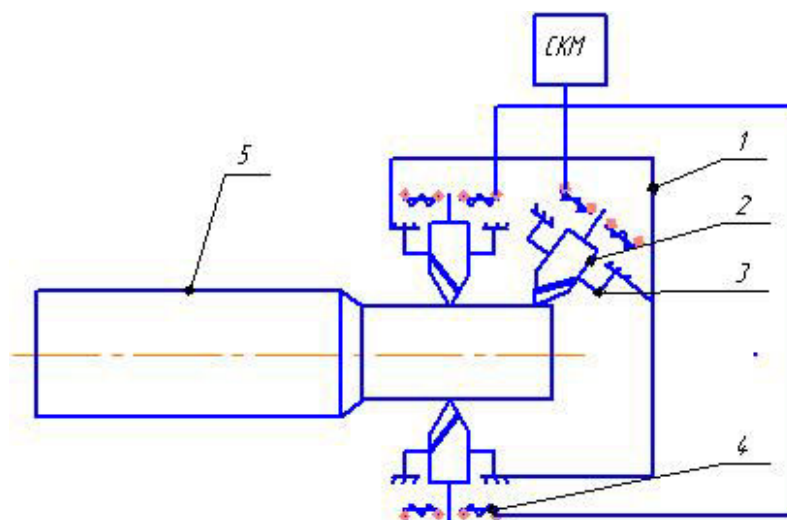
Схема обробки циліндричної деталі трирізцевою головкою
